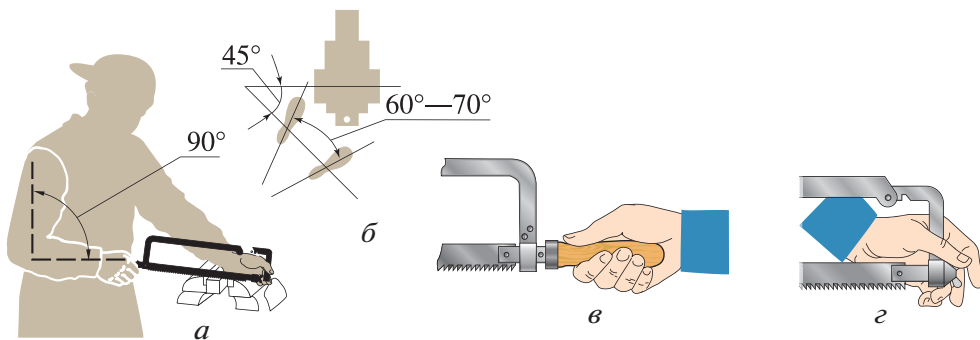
Рабочее положение при резании слесарной ножовкой:
